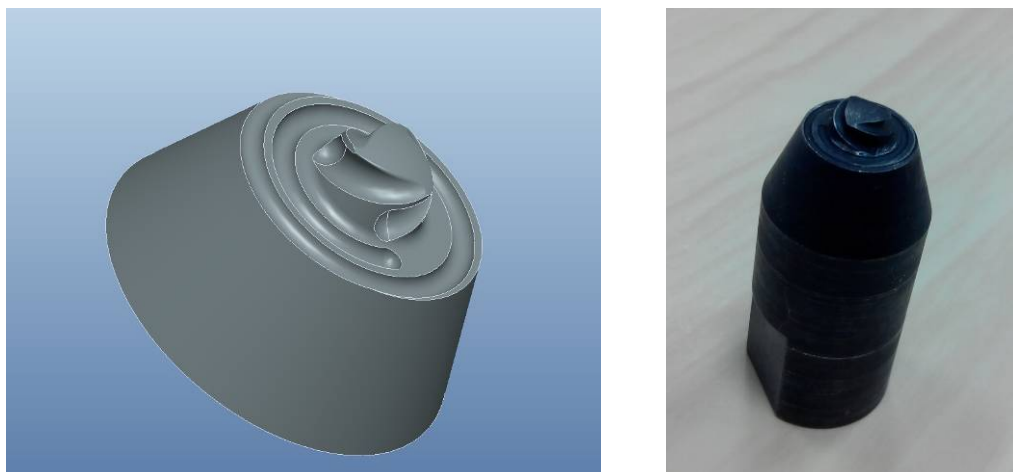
Инструмент для СТП: усеченный конус с крупными резьбовыми насечками
